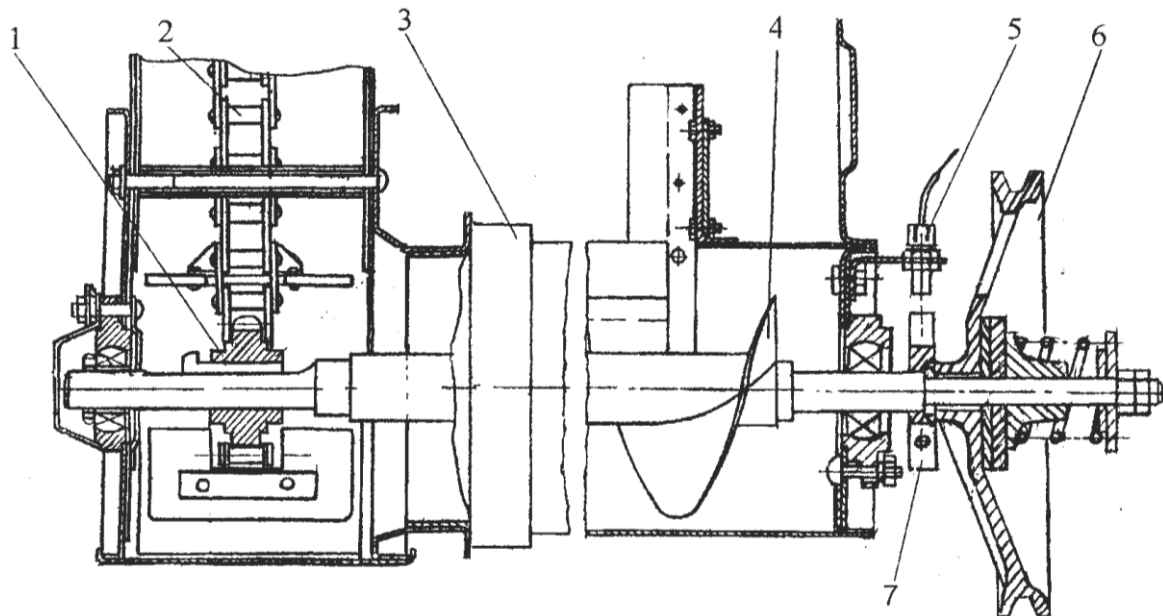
Шнек колосовой: 1 – звездочка; 2 – цепь элеватора; 3 – кожух; 4 – шнек; 5 – индуктивный датчик; 6 – шкив; 7 – формиратор сигналов
